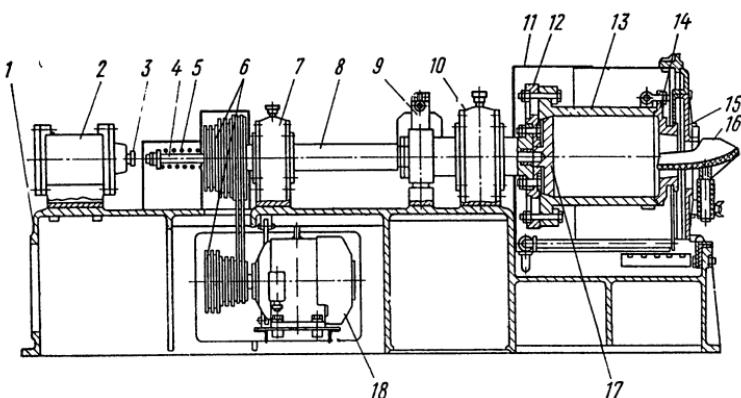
Центробежная машина для отливки цилиндрических заготовок
